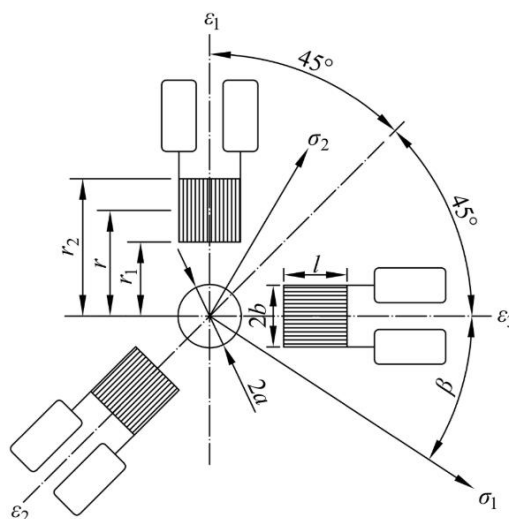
Устройство тензодатчика для метода сверления отверстий [21]
